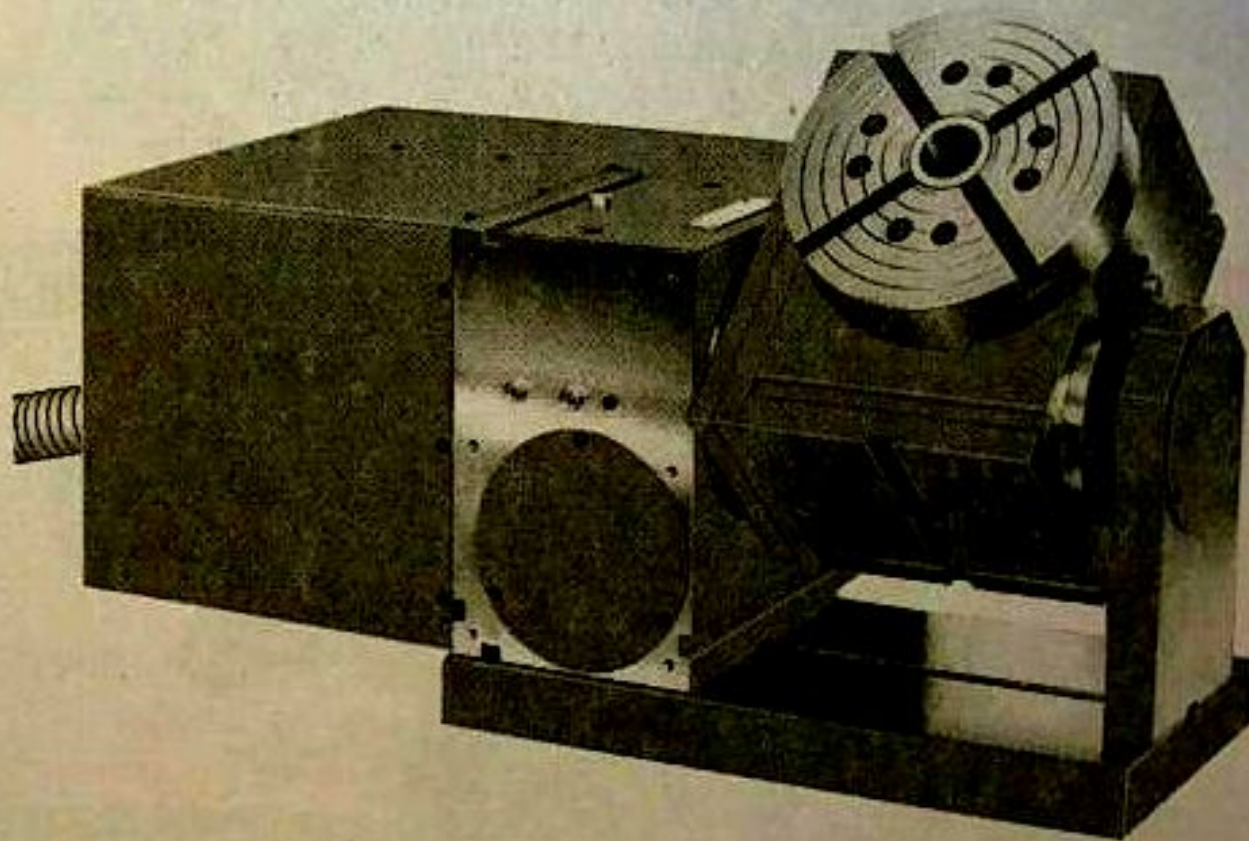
Универсальное приспособление для обработки заготовок различных диаметров под разными углами
